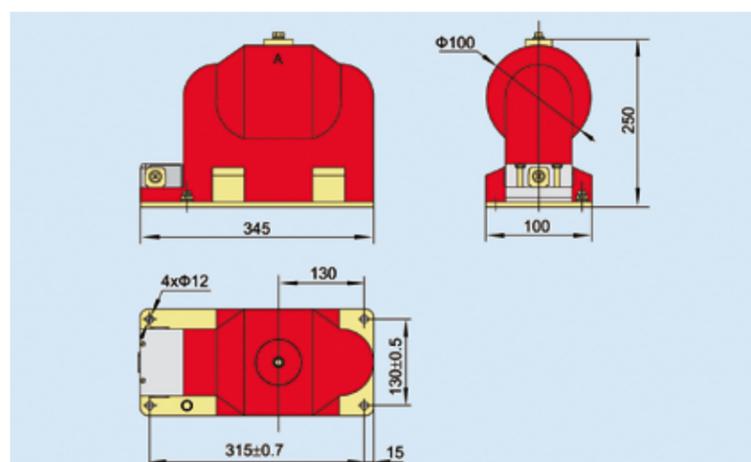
Внешний вид и размеры трансформатора напряжения JDZX9-10
